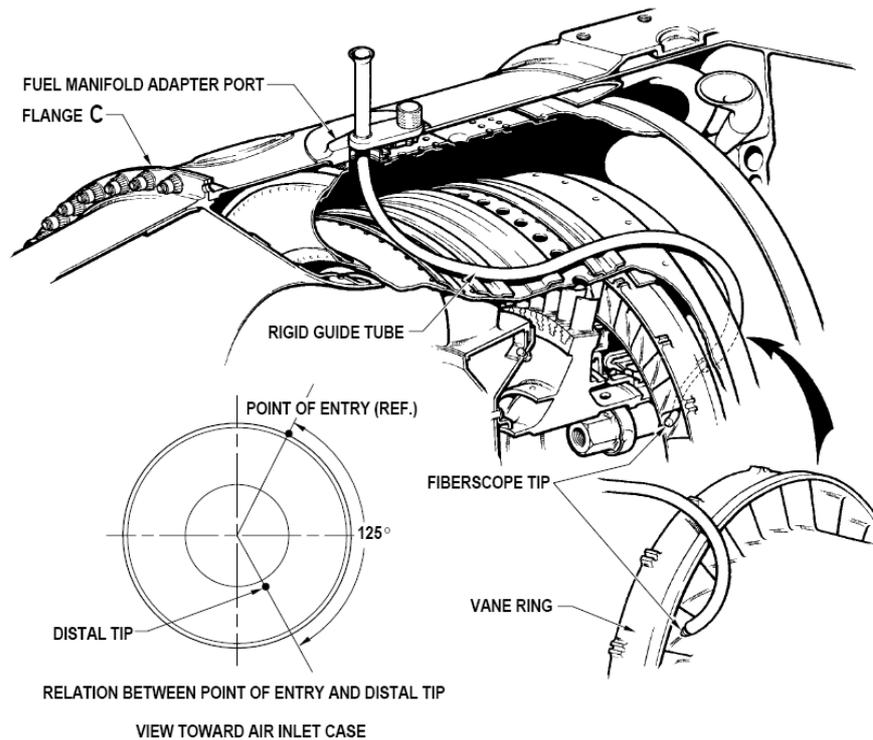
Inspection de la chambre de Combustion et la turbine
